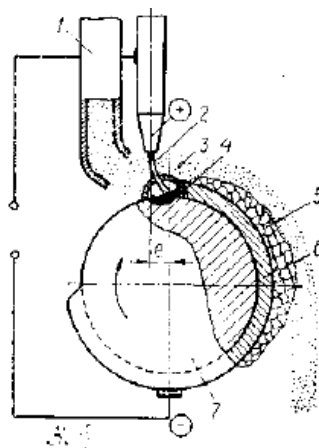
Наплавлення під шаром флюсу:
